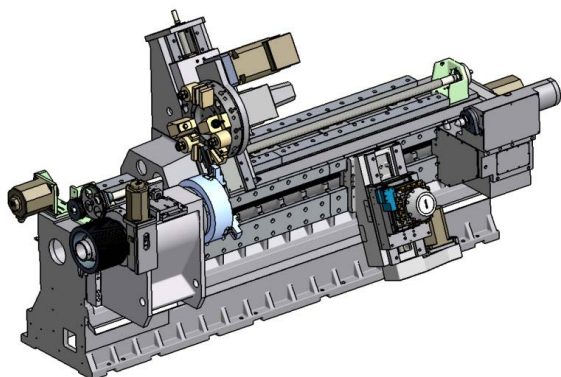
Компоновка центра токарного двухсуппортного, с устройством позиционирования и круговой подачей шпинделя (осью С), револьверными головками для токарного и приводного инструмента на верхнем и нижнем суппортах
